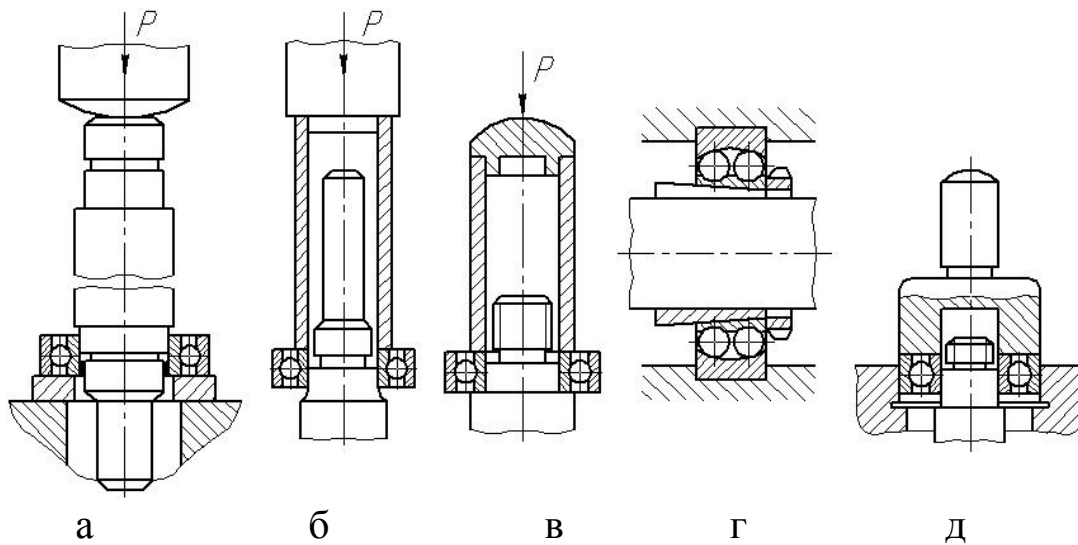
Встановлення підшипників на вал і в корпус деталі
